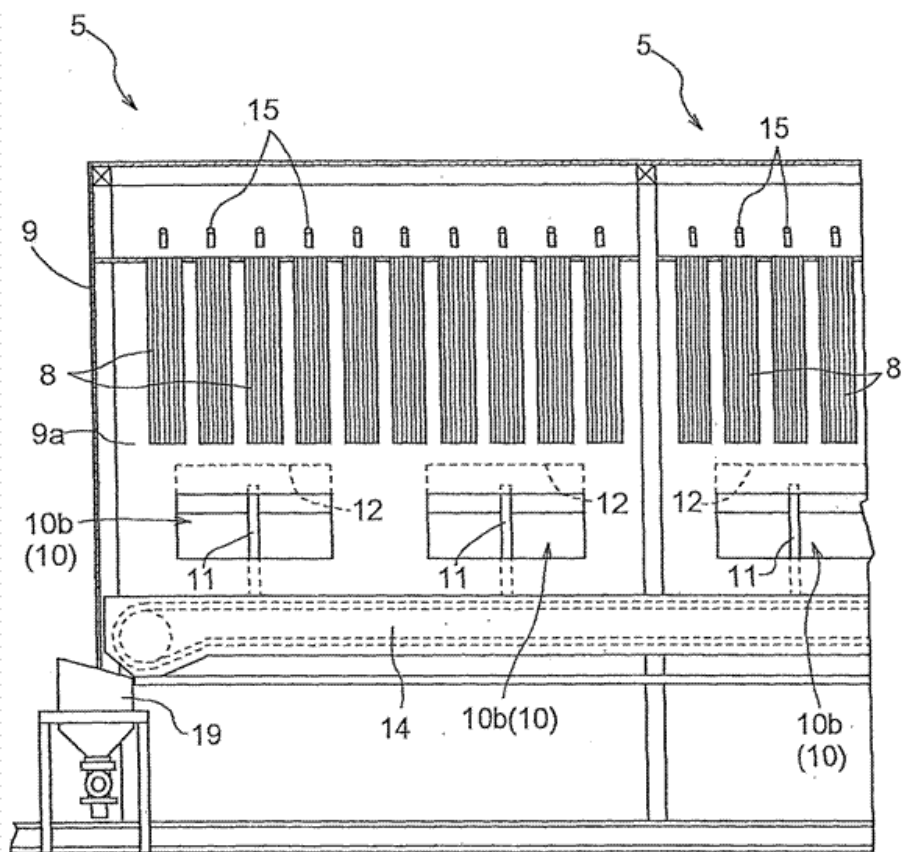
увеличенный вид главного участка окрасочной камеры.
